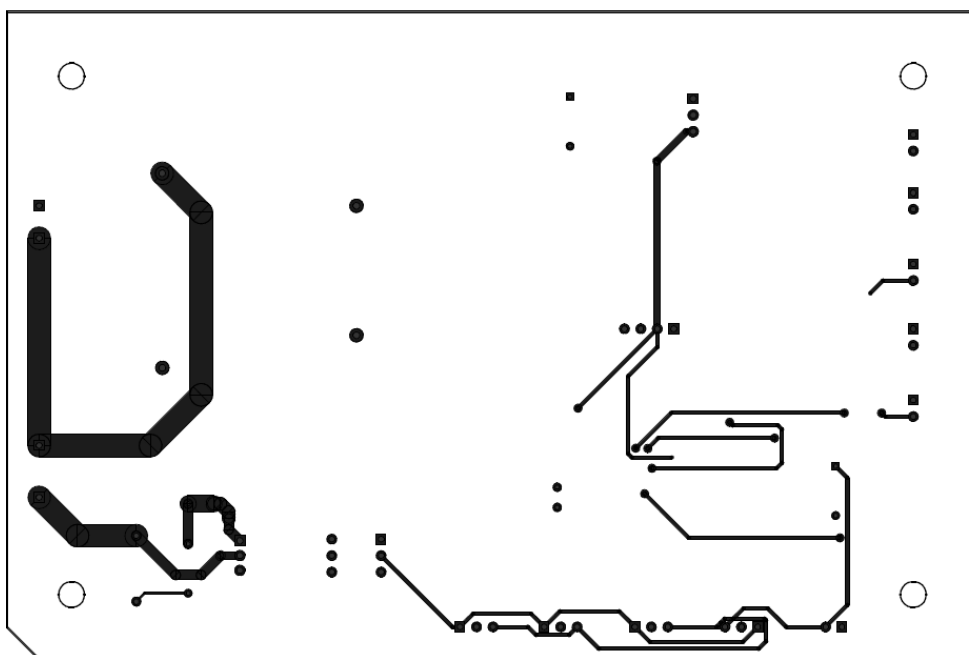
Вид на печатную плату генератора размагничивающего тока
